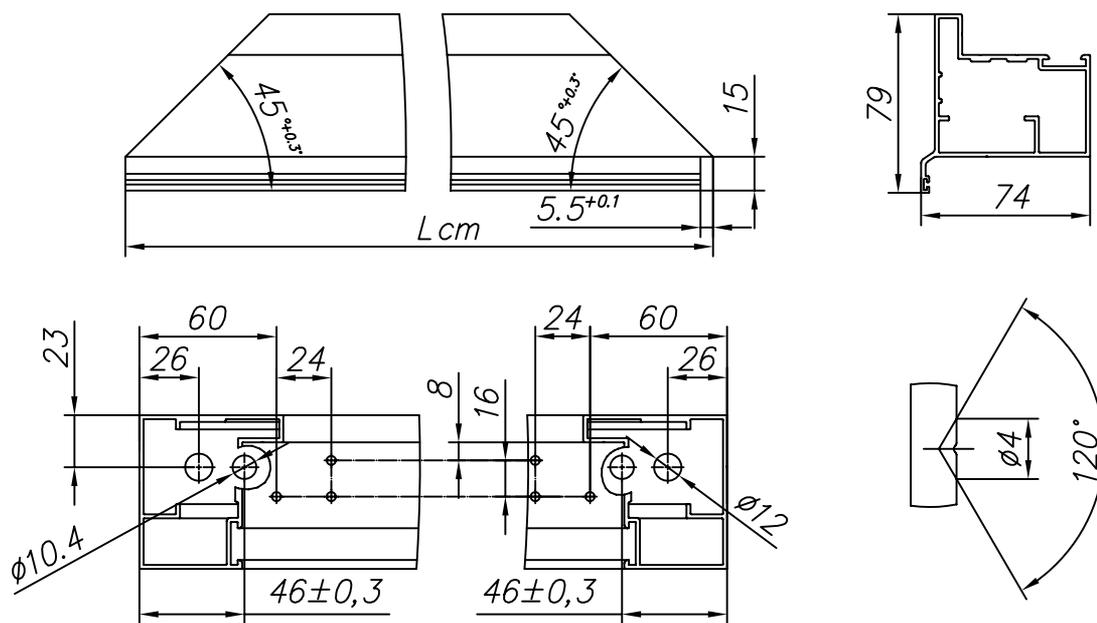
Изготовление стойки (профиль рамы FLGU.400.0111)
